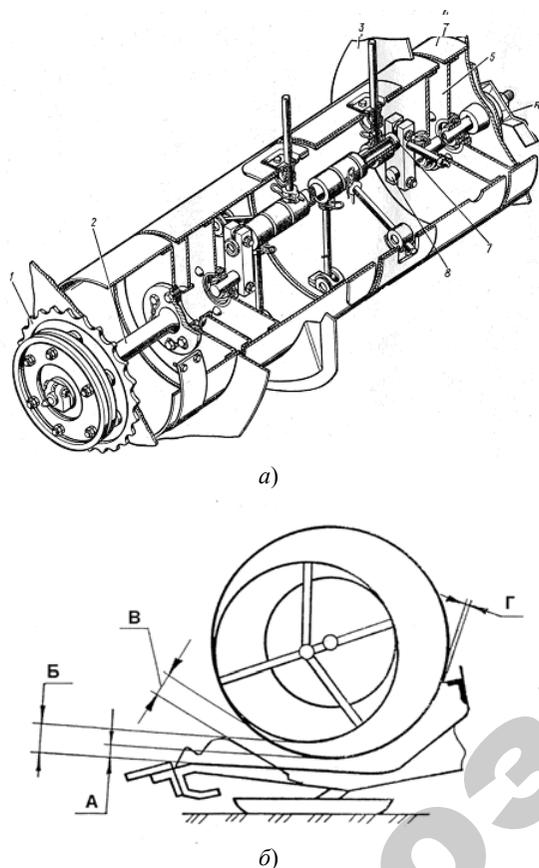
Шнек: *a* — конструкция шнека; 1 — звездочка приводная с предохранительной муфтой; 2 — цапфа; 3 — лента спиральная; 4 — корпус; 5 — диск; 6 — рычаг пальчикового механизма; 7 — ось коленчатая пальчикового механизма; 8 — ось управления пальчиковым механизмом; *б* — схема расположения шнека и его пальчикового механизма при работе жатки: А — зазор между витками шнека и днищем жатки; Б, В — зазор между пальцами шнека и днищем жатки; Г — зазор между витками шнека и чистиком
